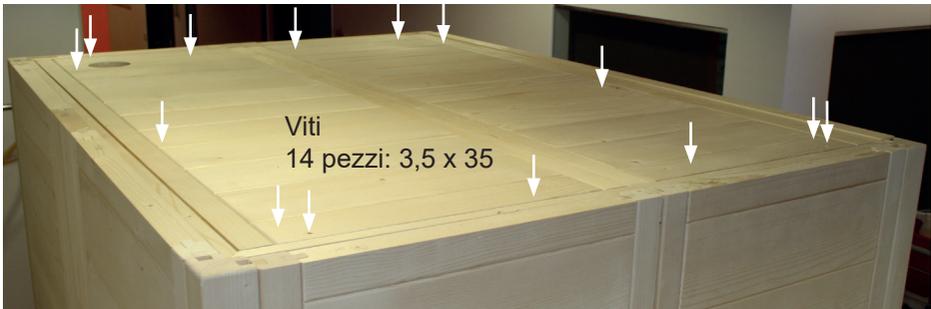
Inserimento dell'elemento tetto anteriore
